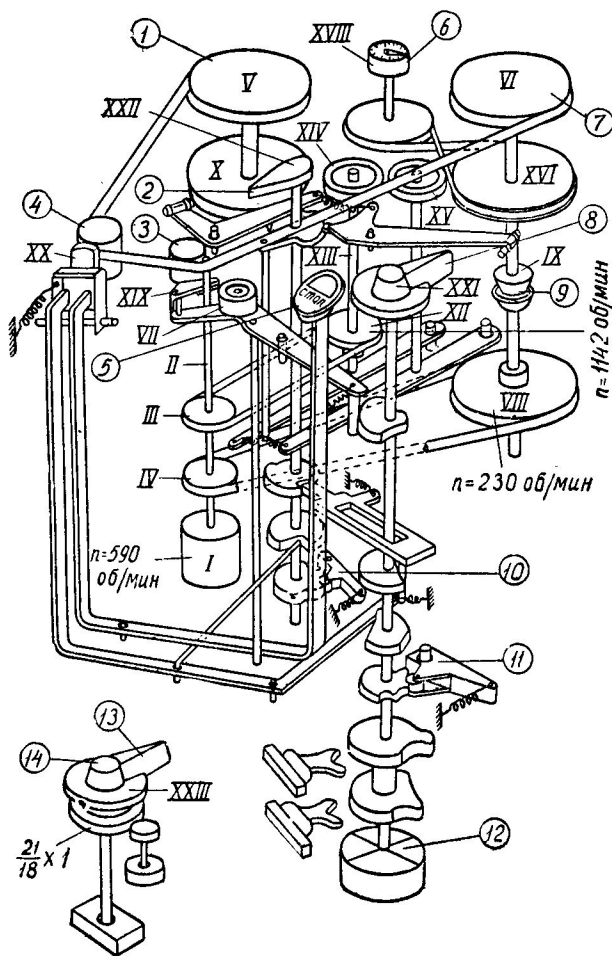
Кинематическая схема лентопротяжного механизма: 1 — подающая кассета; 2 — рукоятка управления ускоренной и обратной перемотки; 3 — универсальная головка; 4 — стирающая головка; 5 — педаль временной остановки; 6 — счетчик; 7 — принимающая кассета; 8 — рукоятка перевода рода работы; 9 — муфта проскальзывания; 10 — фиксатор на три положения; 11 — фиксатор на четыре положения; 12 — переключатель рода работы; 13 — регулятор громкости; 14 — регулятор тембра
